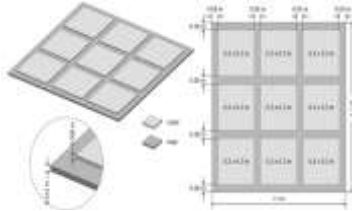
Skema dimensi plat baja dek kapal dan lapisan bahan semen
